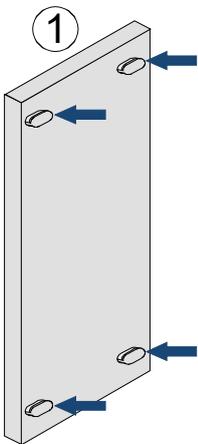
Rückseite Basis-Modulträger mit vier Halterungen (Art.-Nr. FX808321)
